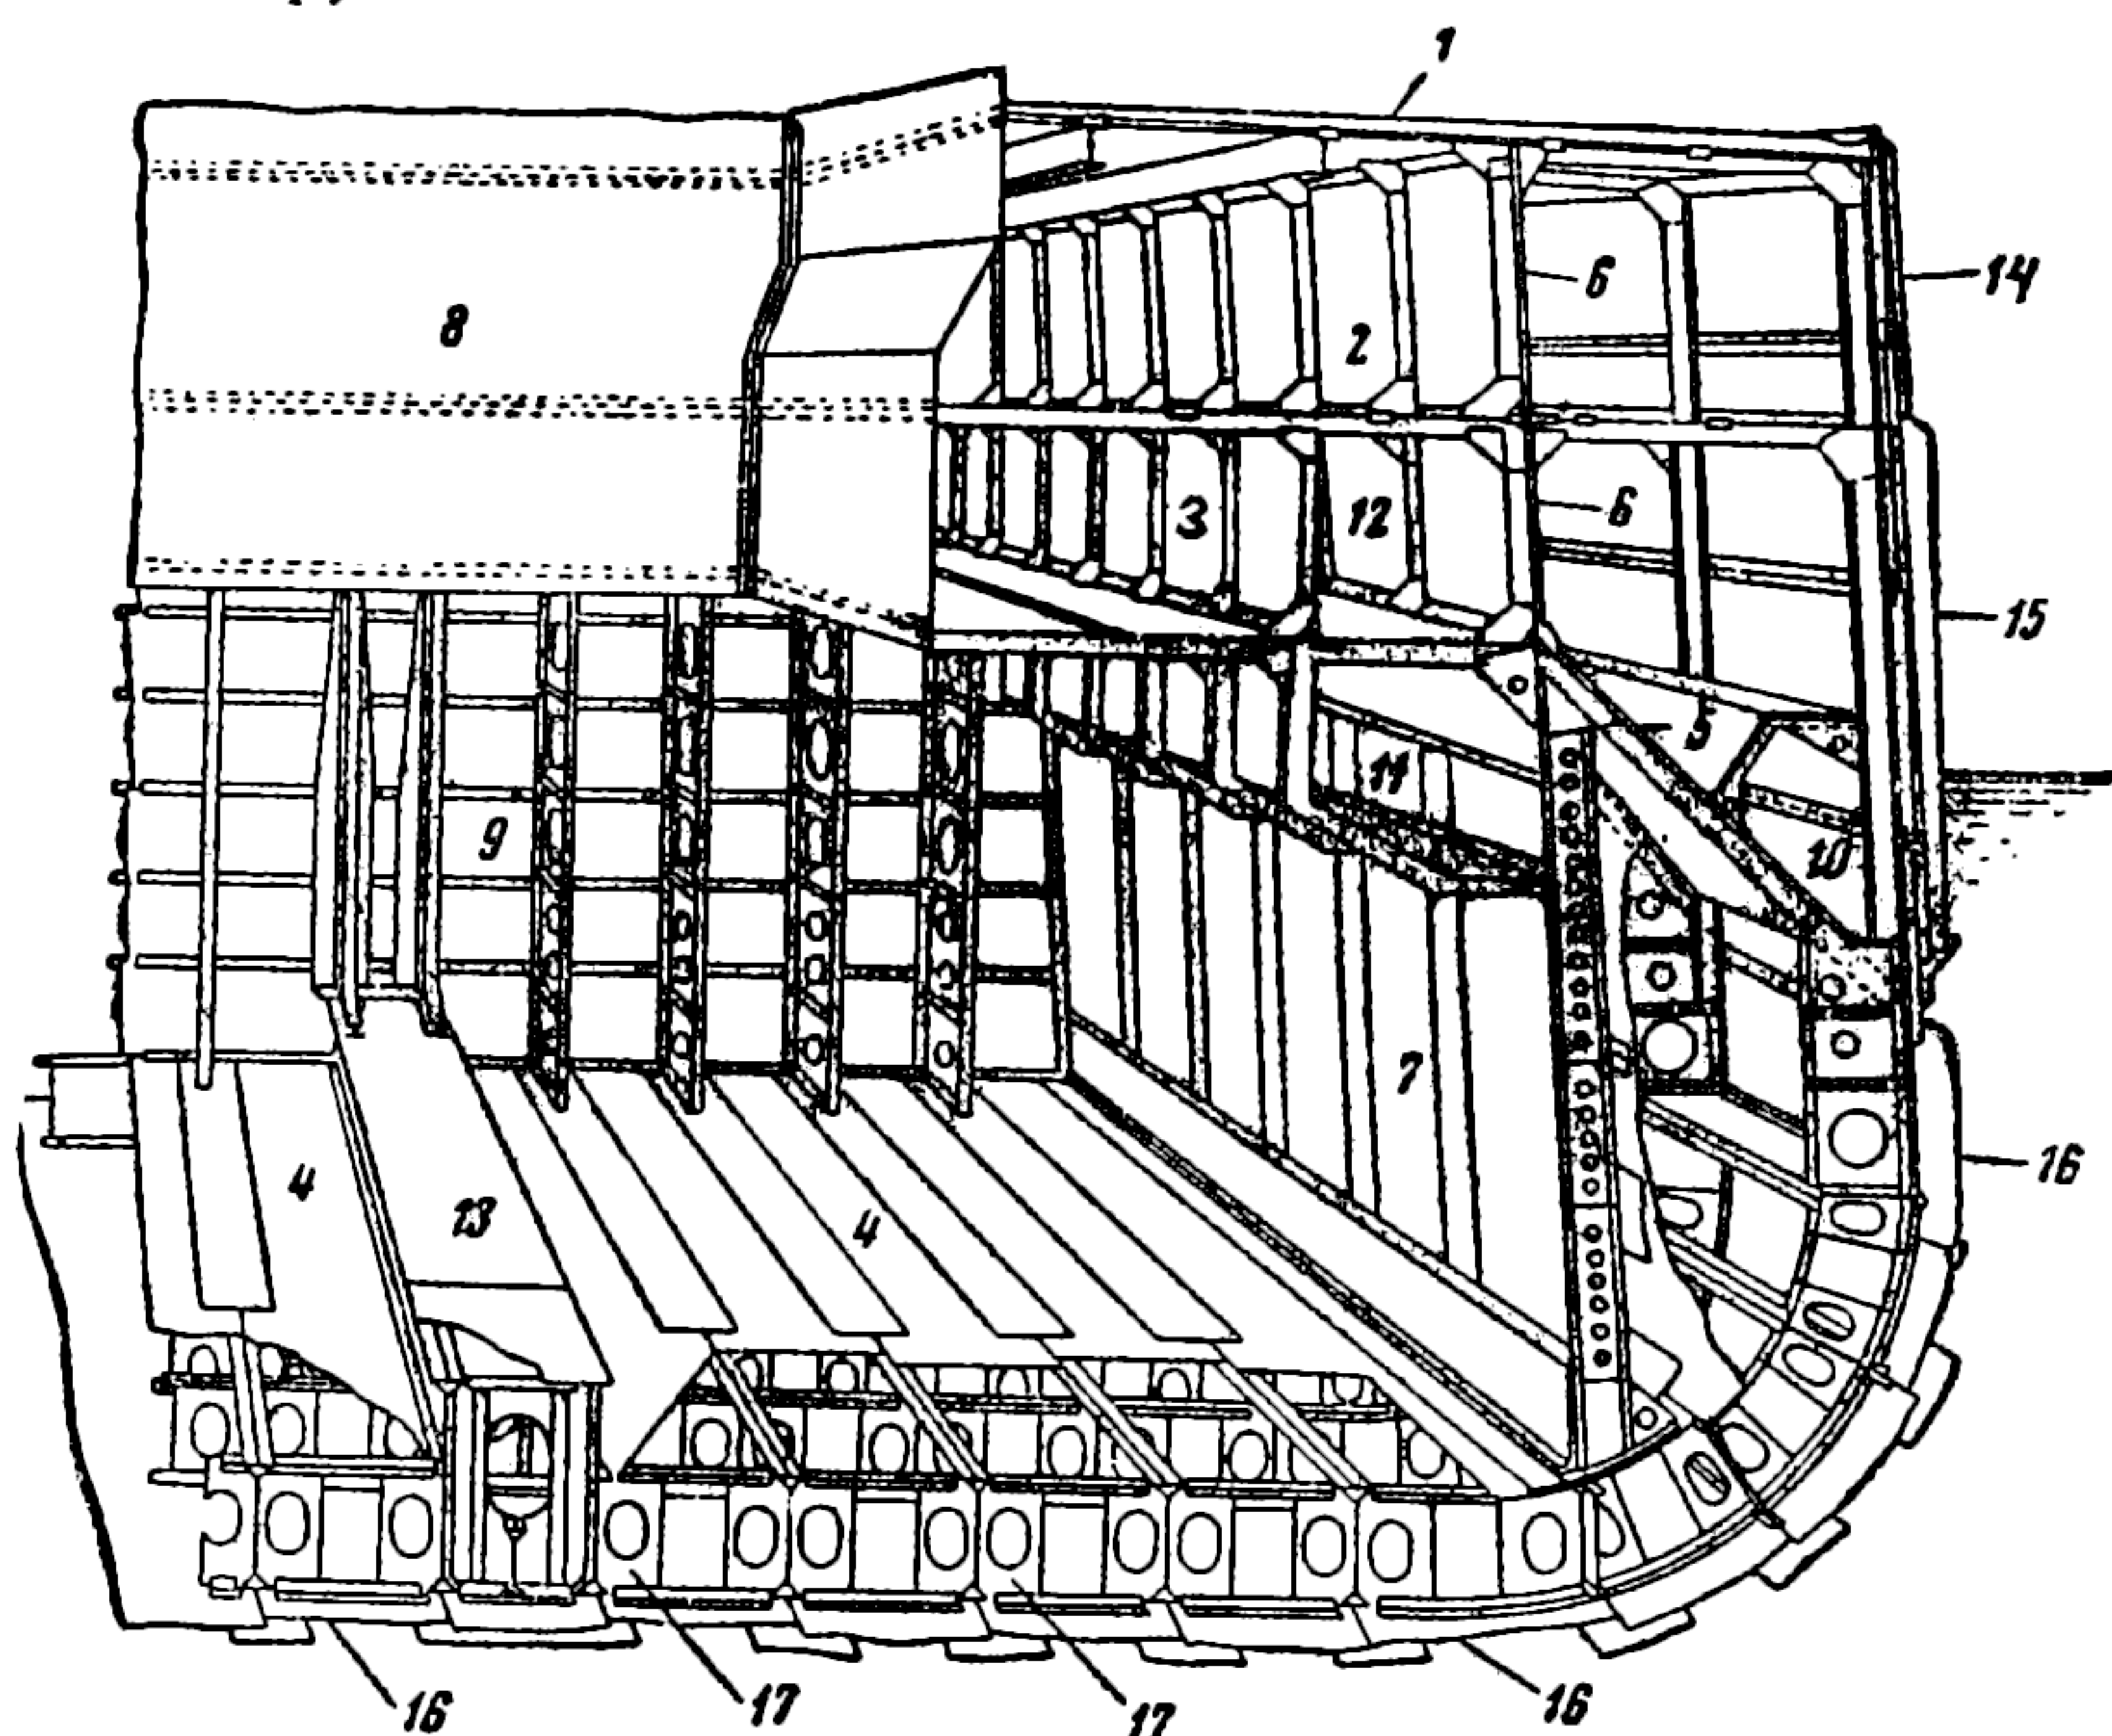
Схема устройства главных частей линейного корабля. Современ-
